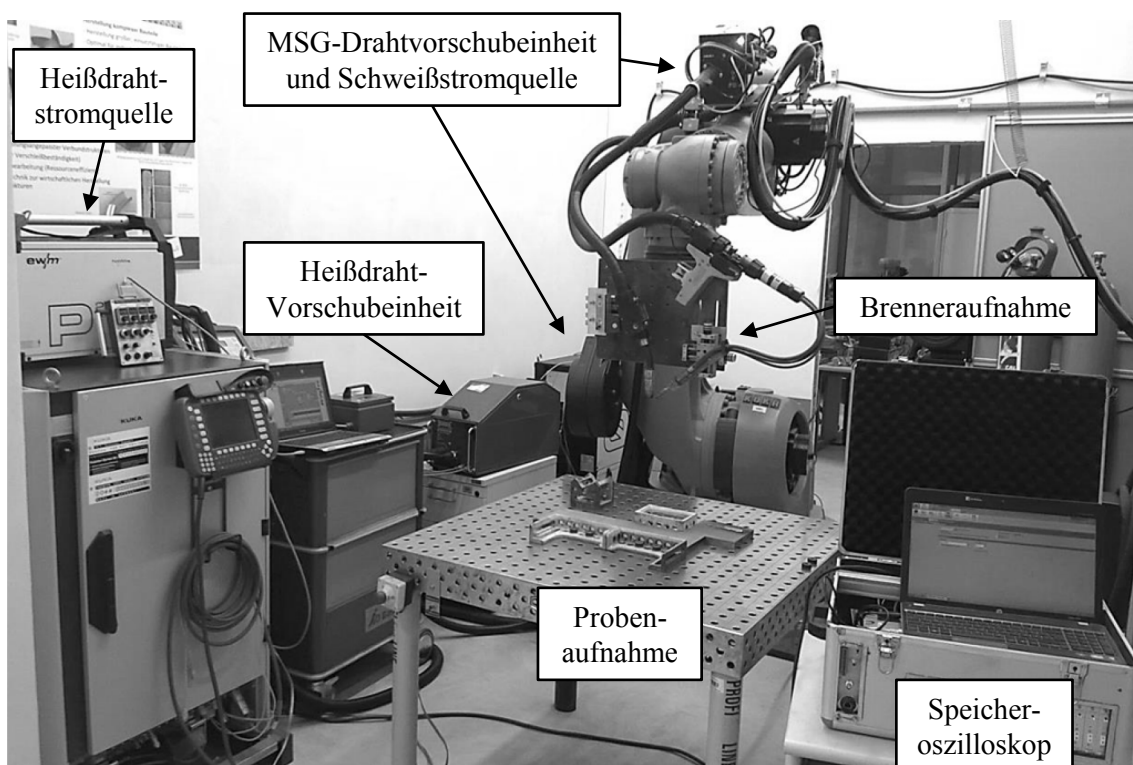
Versuchsaufbau für das flächige Auftragschweißen, welches mit einem Roboter „KUKA KR150-S“ umgesetzt wurde.
